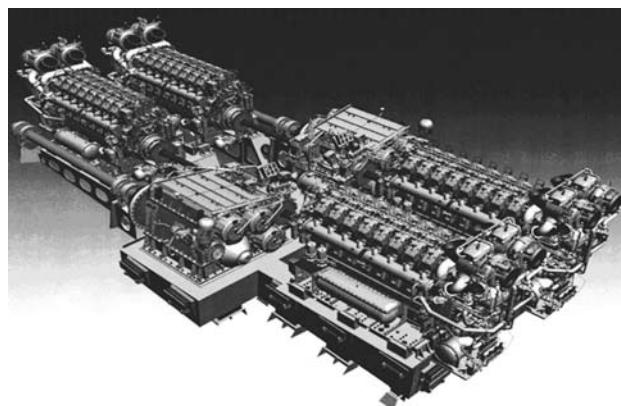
Главная энергетическая установка 2x1ДДА12000 на базе четырех двигателей 16Д49 и двух реверс-редукторных передач
